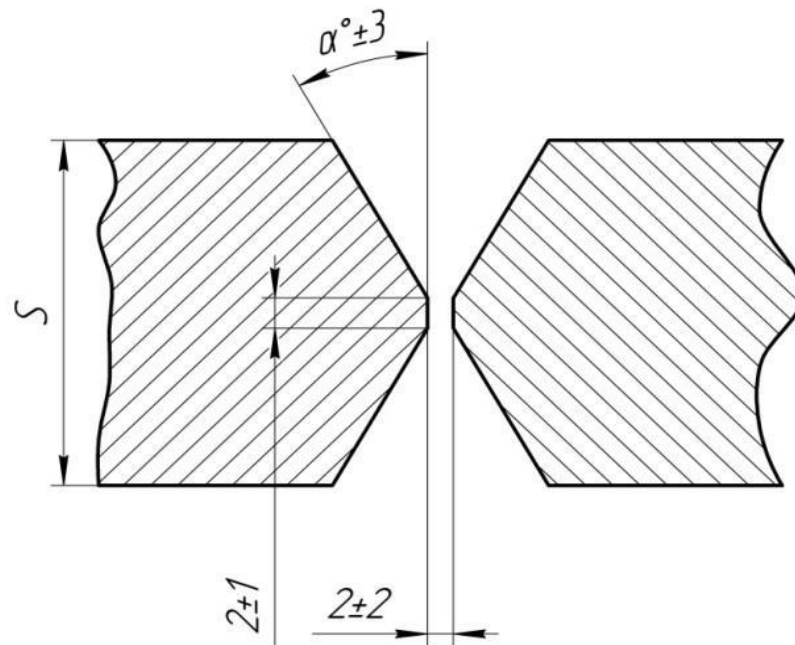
Стикове зварне з'єднання з двома симетричними скосами кромки типу С25
